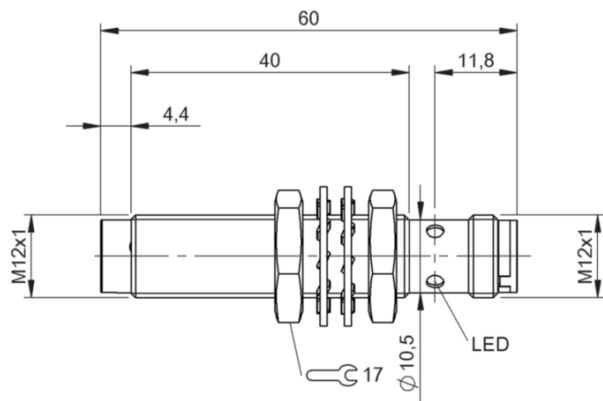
Aufbau Typen mit nicht bündigem Einbau
